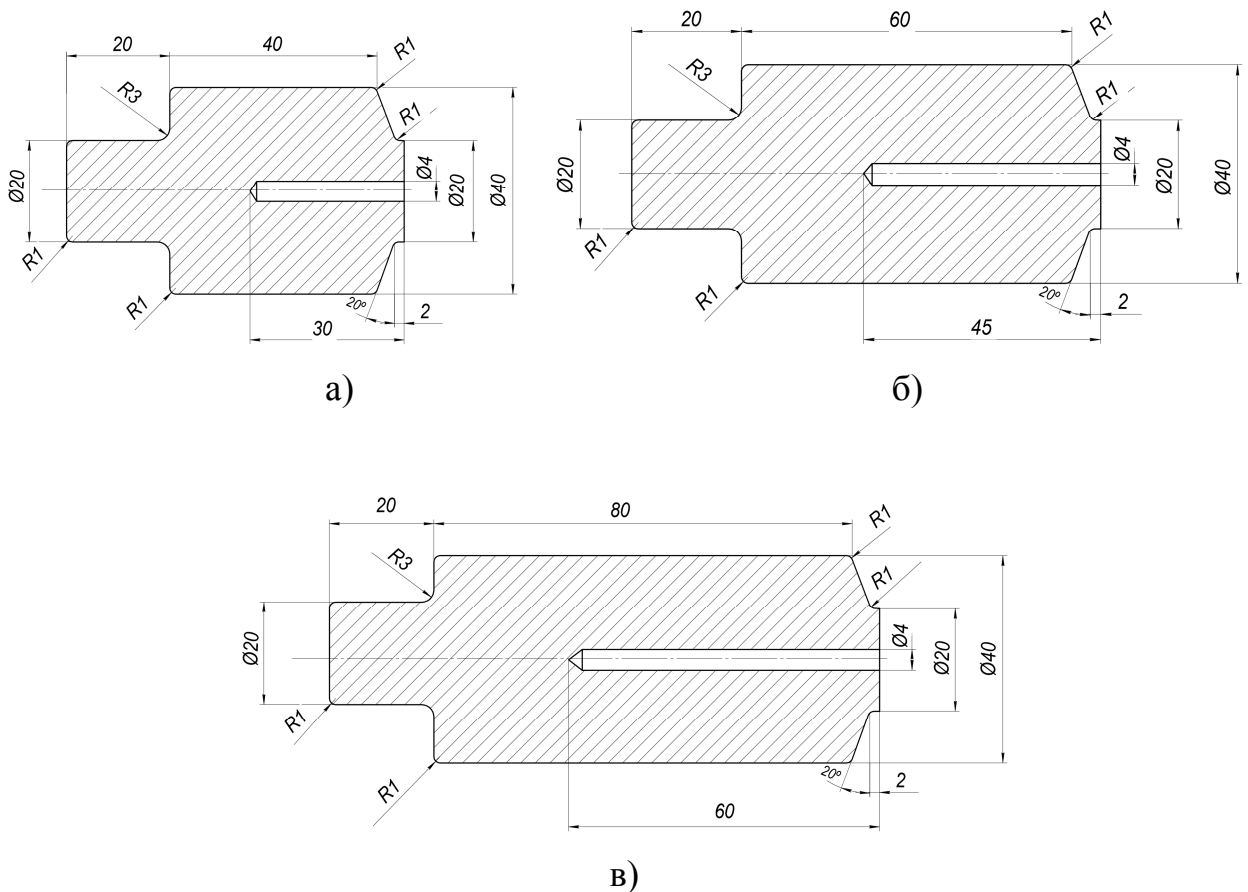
Эскизы заготовок с различным соотношением H / D (а – в) и модели из стали с искусственным осевым дефектом
